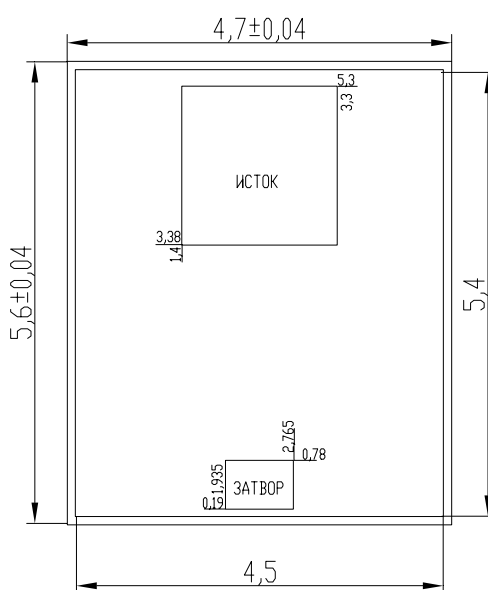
Габаритный чертеж кристалла 2П7172А-5
